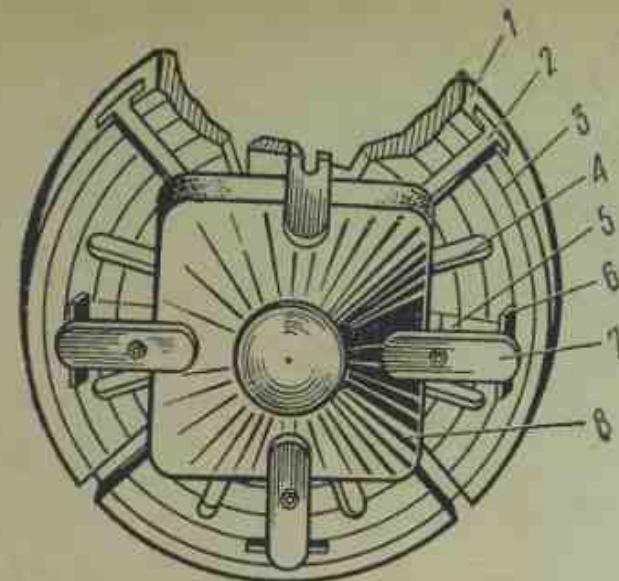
Установка заготовки некруглой формы на планшайбе:
